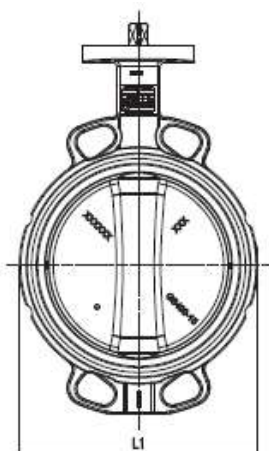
Габаритные и присоединительные размеры затворов дисковых поворотных типа VFY (SYLAX)
